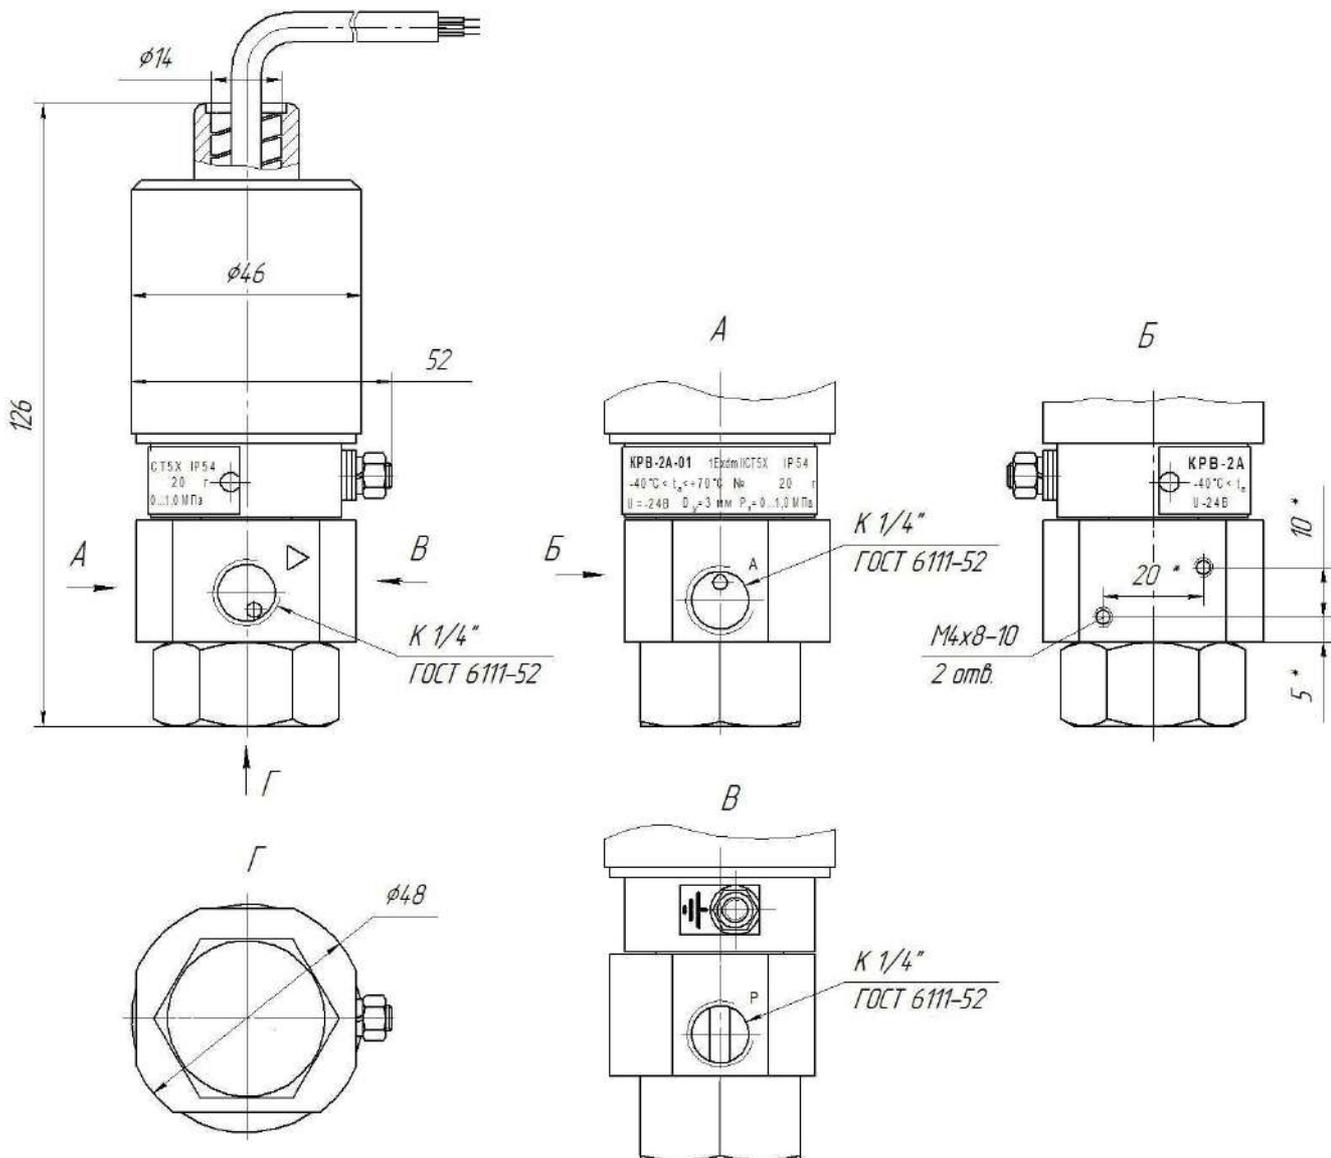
Габаритные и присоединительные размеры клапана КРВ-2А
